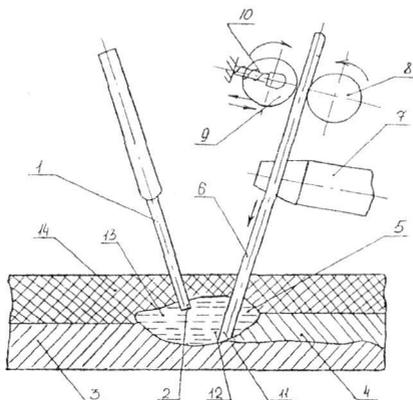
Схема устройства для осуществления способа наплавки с непрерывно расходуемым ультразвуковым волноводом-излучателем: 1 – электродная проволока; 2 – конец электродной проволоки; 3 – наплавляемый образец; 4 – наплавленный металл; 5 – ванна расплавленного металла; 6 – присадочная проволока; 7 – волновод; 8 – приводной ролик; 9 – прижимной ролик; 10 – пружина; 11 – конец волноводной проволоки; 12 – поверхность наплавляемого образца
